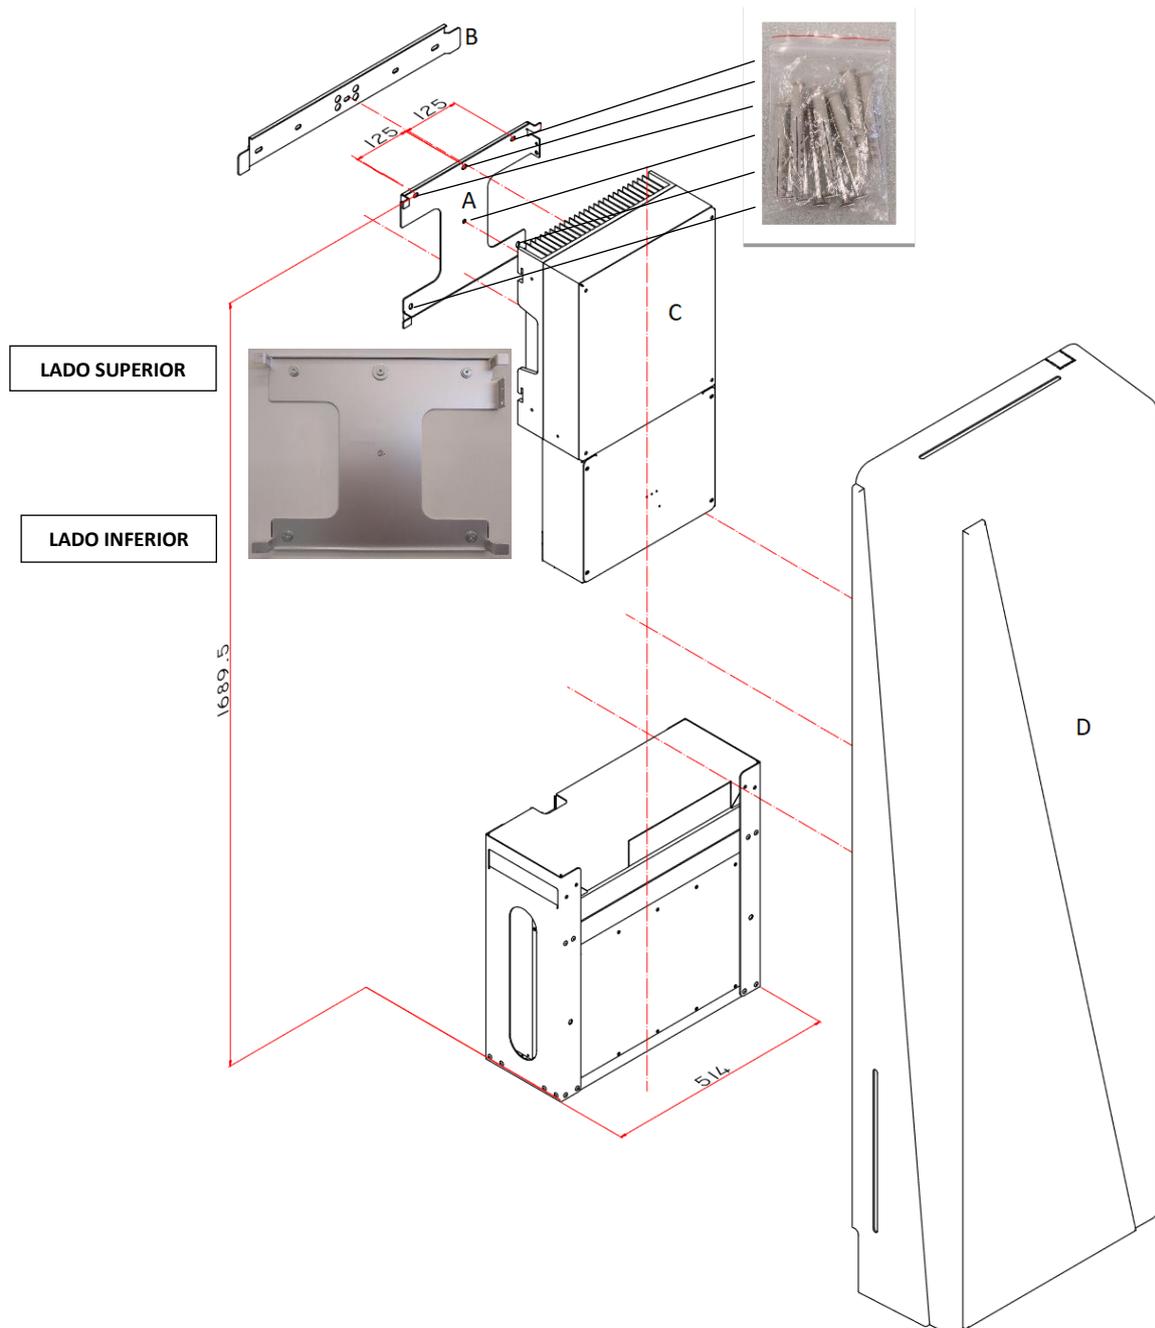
Distancia de montaje entre la abrazadera inverter y la plataforma
